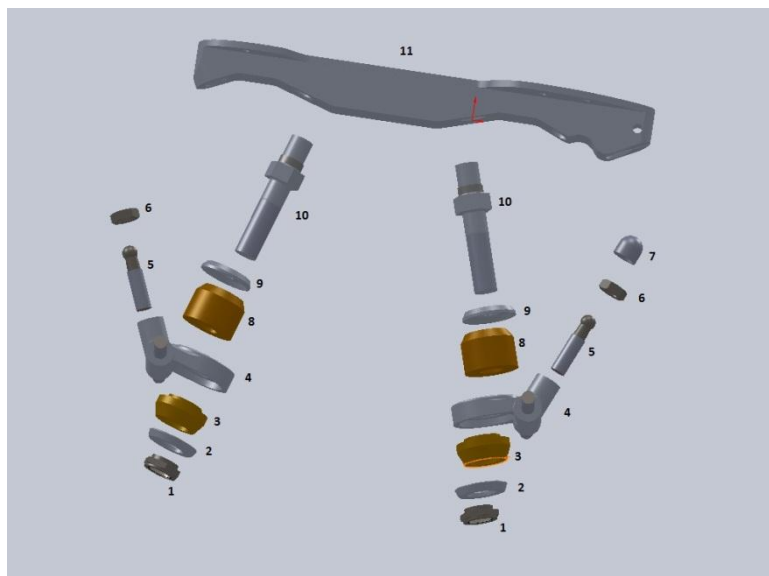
Vista explodida do patim de corpo em alumínio maquinado
